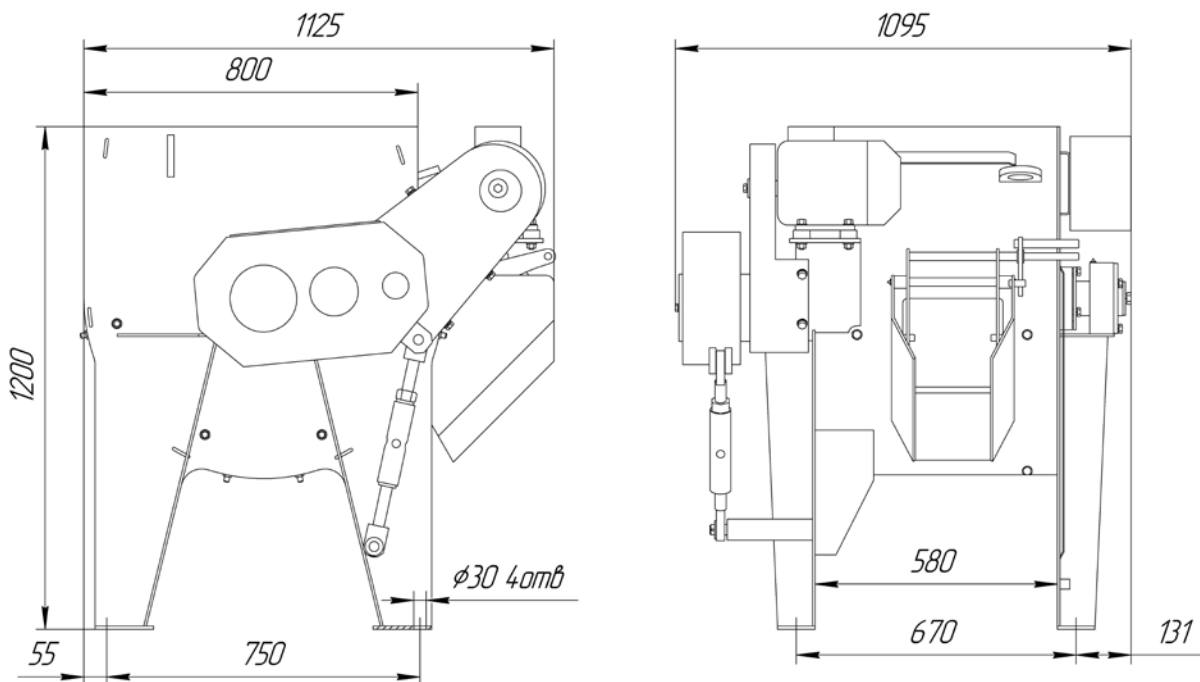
Габаритно-присоединительные размеры СГ-150.
